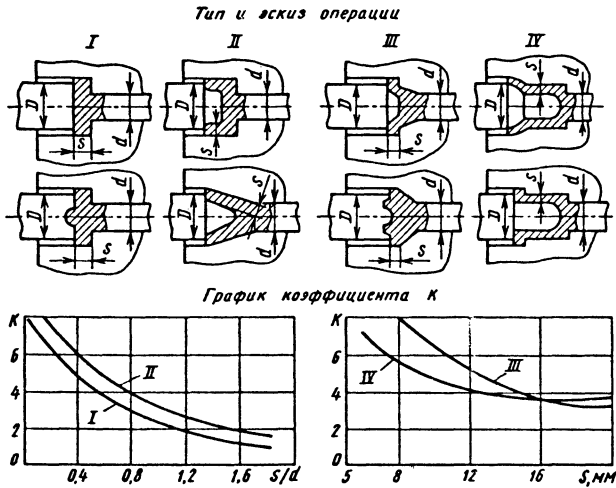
К определению усилия штамповки на ГKM в закрытых формовочных ручьях для высадки и прошивки (по В. И. Залесскому)
